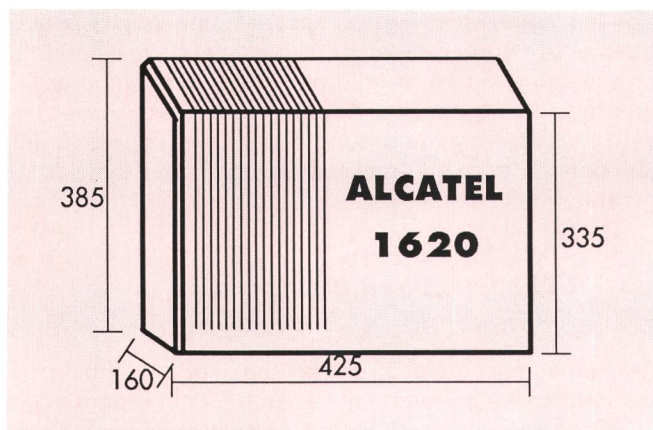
Dimensions du boîtier – Dimensioni del contenitore
